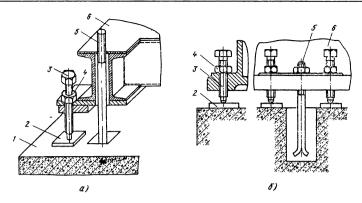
Применение регулировочных винтов для установки сварных (a) и литых (b) конструкций:
